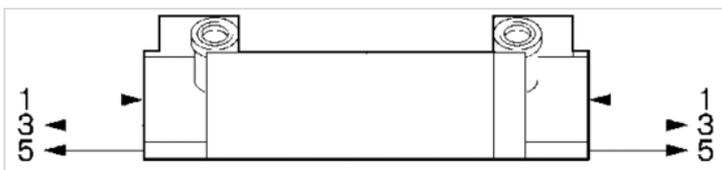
Gewindeanschlüsse 1 3 und 5 axial und von oben
